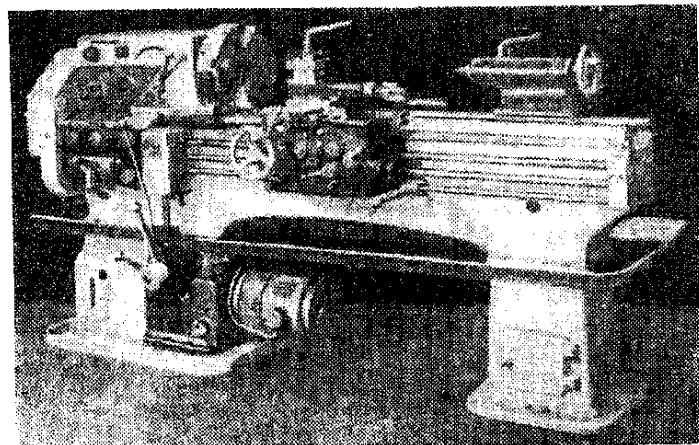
Прецизионный токарный станок со станиной из магниевых сплавов
